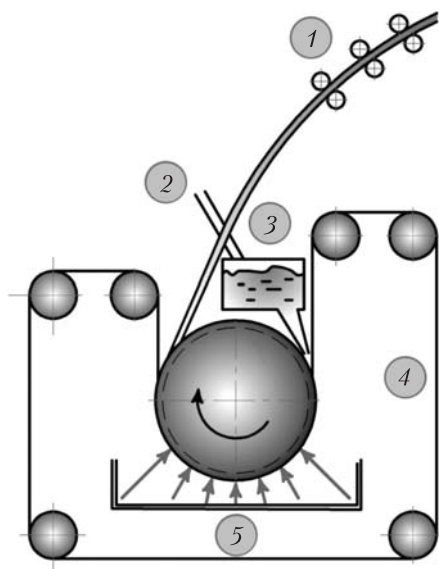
Схема непрерывной разливки меди на колесо: 1 – получаемая заготовка; 2 – подача меди от ковша; 3 – промежуточный ковш; 4 – стальная лента; 5 – зона водяного охлаждения
